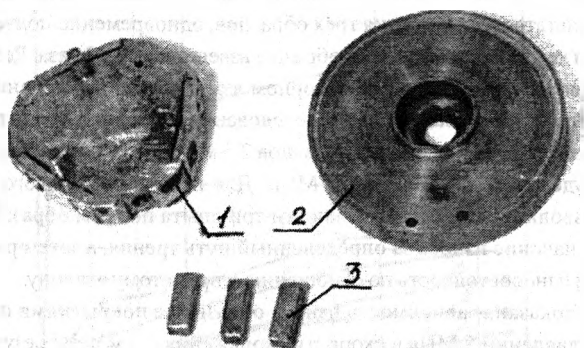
Внешний вид державки, контртела и исследуемых образцов:
